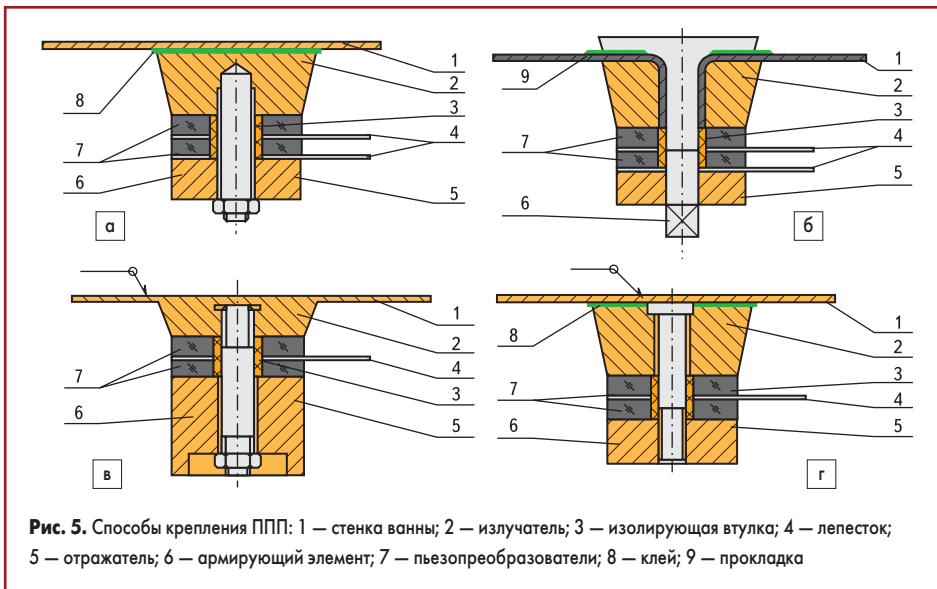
Способы крепления ППП: 1 — стенка ванны; 2 — излучатель; 3 — изолирующая втулка; 4 — лепесток; 5 — отражатель; 6 — армирующий элемент; 7 — пьезопреобразователи; 8 — клей; 9 — прокладка
